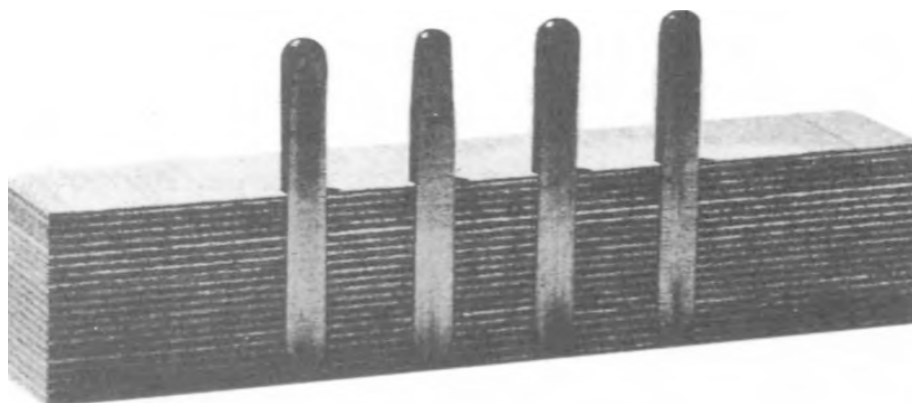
Невеликий фрагмент заготовки стандартного пінблоку рояля, що демонструє перехресне ламінування твердого клену
